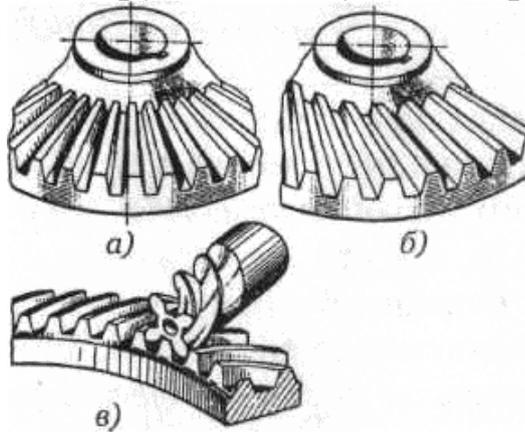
Конические зубчатые колеса: *а* — колесо с прямыми зубьями; *б* — колесо с косыми зубьями; *в* — колесо с круговыми зубьями
